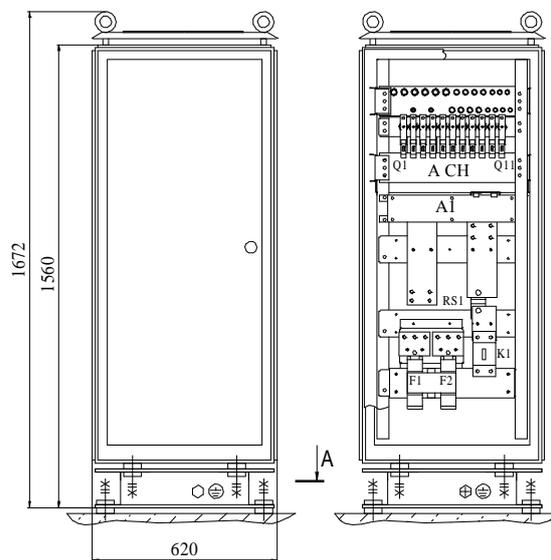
Габаритный чертёж ЩТР-4-У (глубина стойки 620мм)
